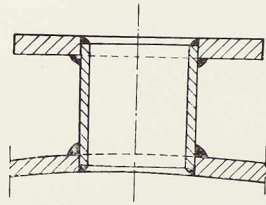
Type de raccordement des nombreuses tubulures du couvercle.
